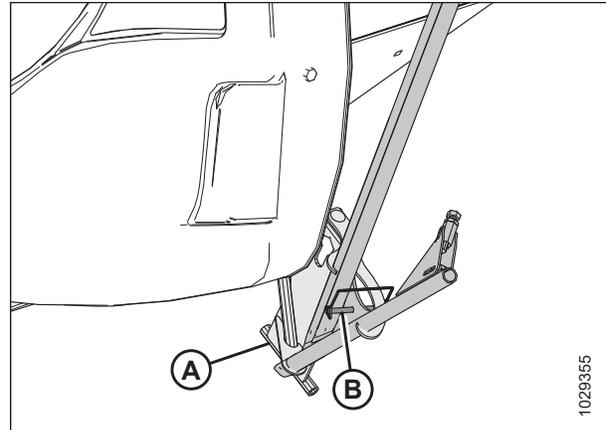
Aufbewahrung Halmteiler für Reis
